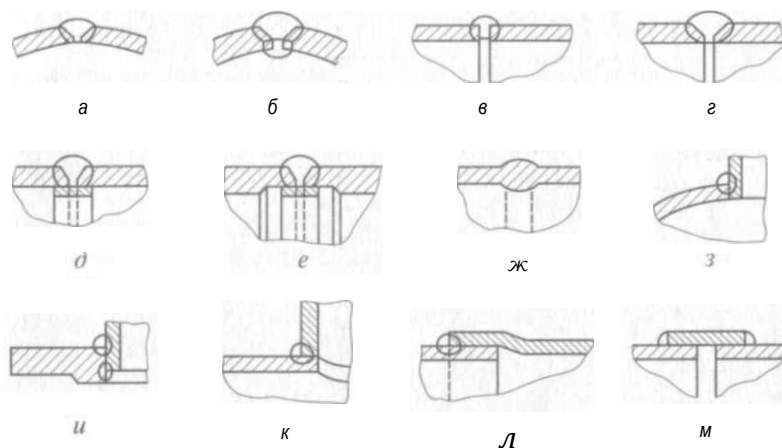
Виды неразъемных сварных соединений труб и деталей трубопроводов:
